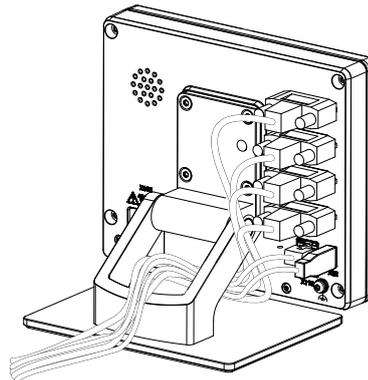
passaggio dei cavi con base di supporto Multi-Pos
